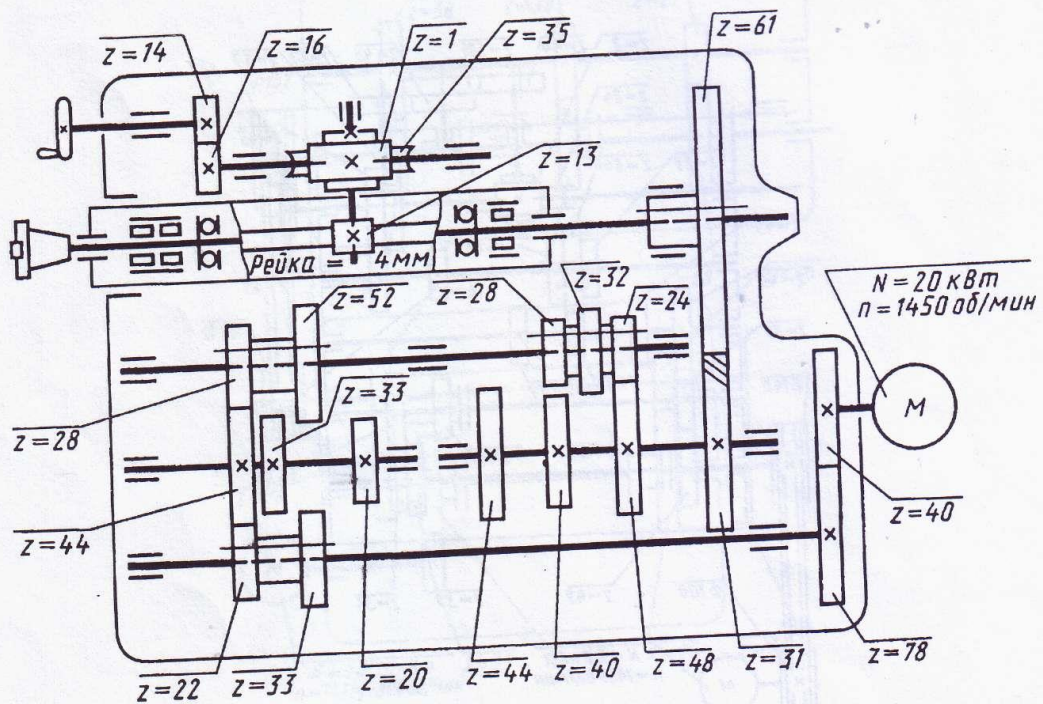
Кинематическая схема коробки скоростей продольно-фрезерного станка 6652
